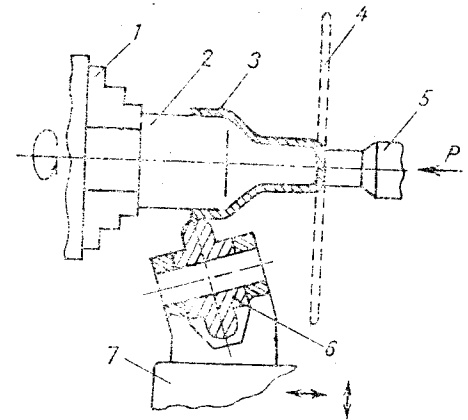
Ротаційне витягування заготовки на токарному верстаті:
